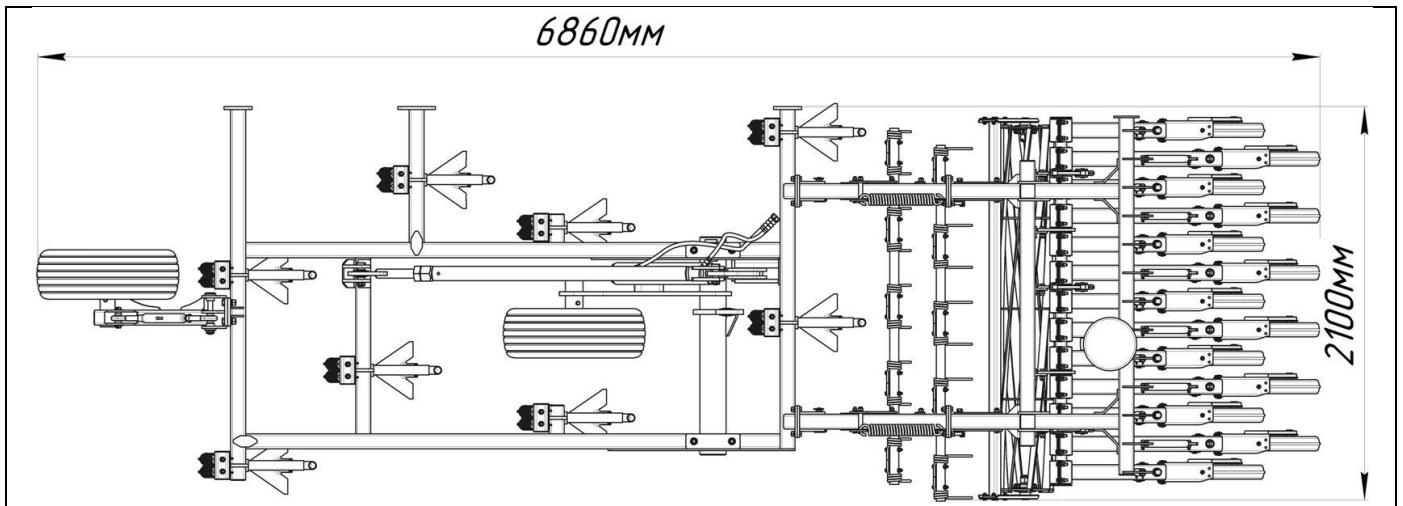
Вид погрузочного места № 2 крыла, при частичной разборке
